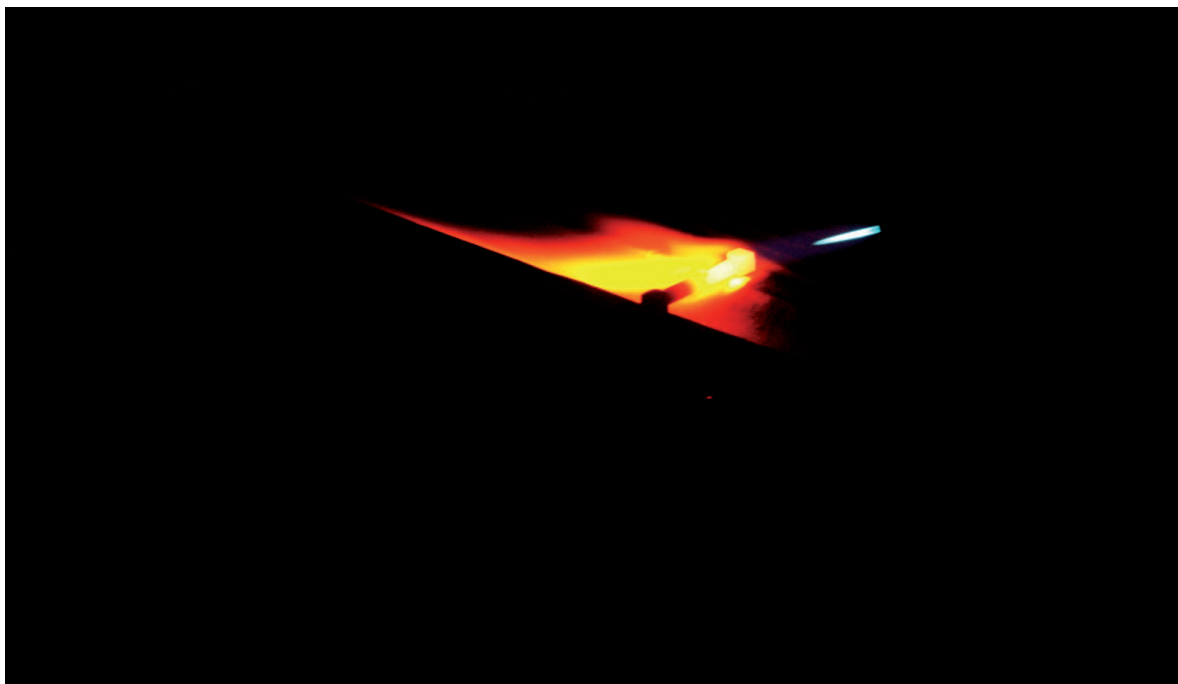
Corpo de prova pré-soldado sendo submetido ao processo de soldagem convencional.
